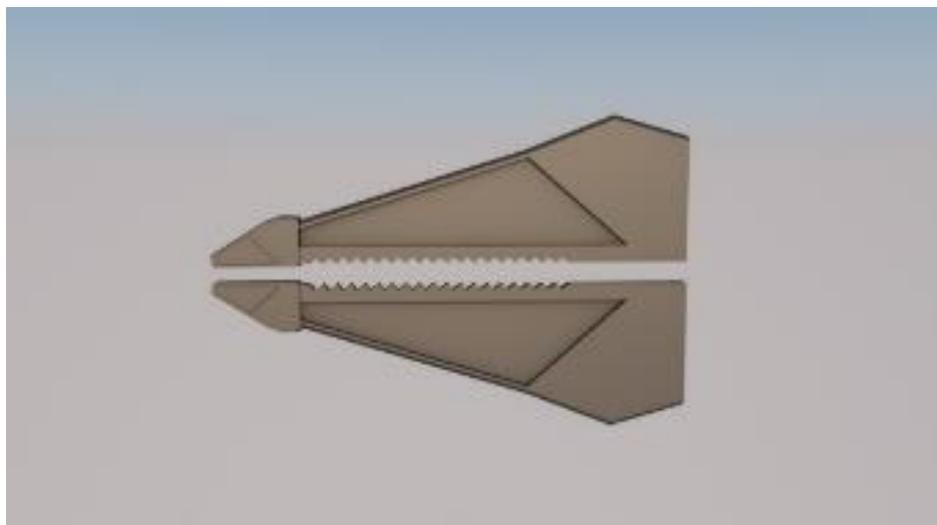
Обратная форма заточки лезвий аварийно-спасательного инструмента (авторская разработка)
